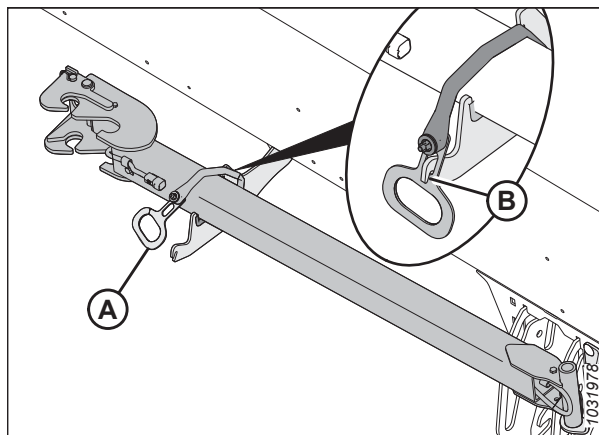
Almacenamiento de la extensión de la barra de remolque
